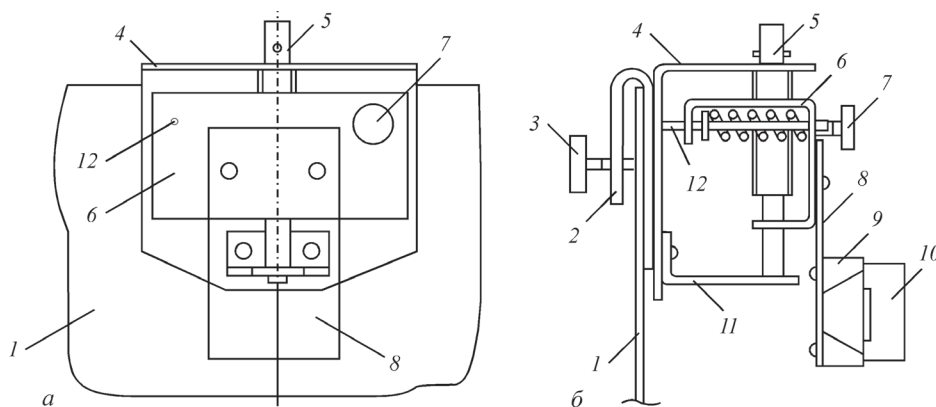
Схема механізму для кріплення та орієнтації рефлекторного перетворювача: а – вид зверху; б – вид збоку
